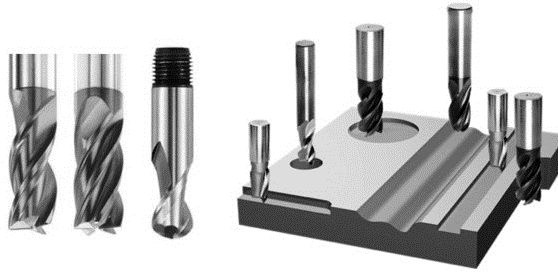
การกัดบ่าฉากและกัดขึ้นรูปสี่เหลี่ยมด้วยดอกกัด Face Milling Cutter
